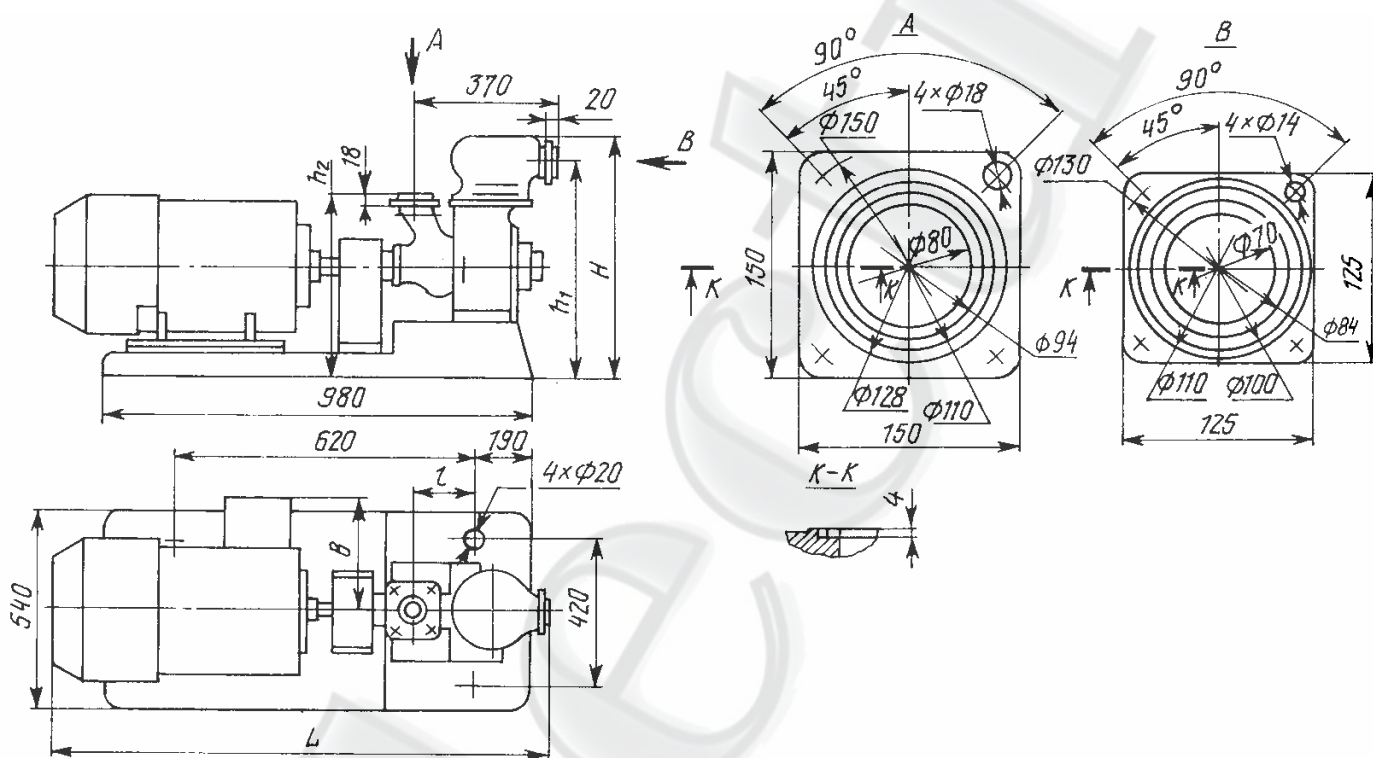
Общий вид, габаритные, присоединительные размеры и масса электронасосного агрегата 1ACЦЛ-20-24Г на железобетонной фундаментной плите
